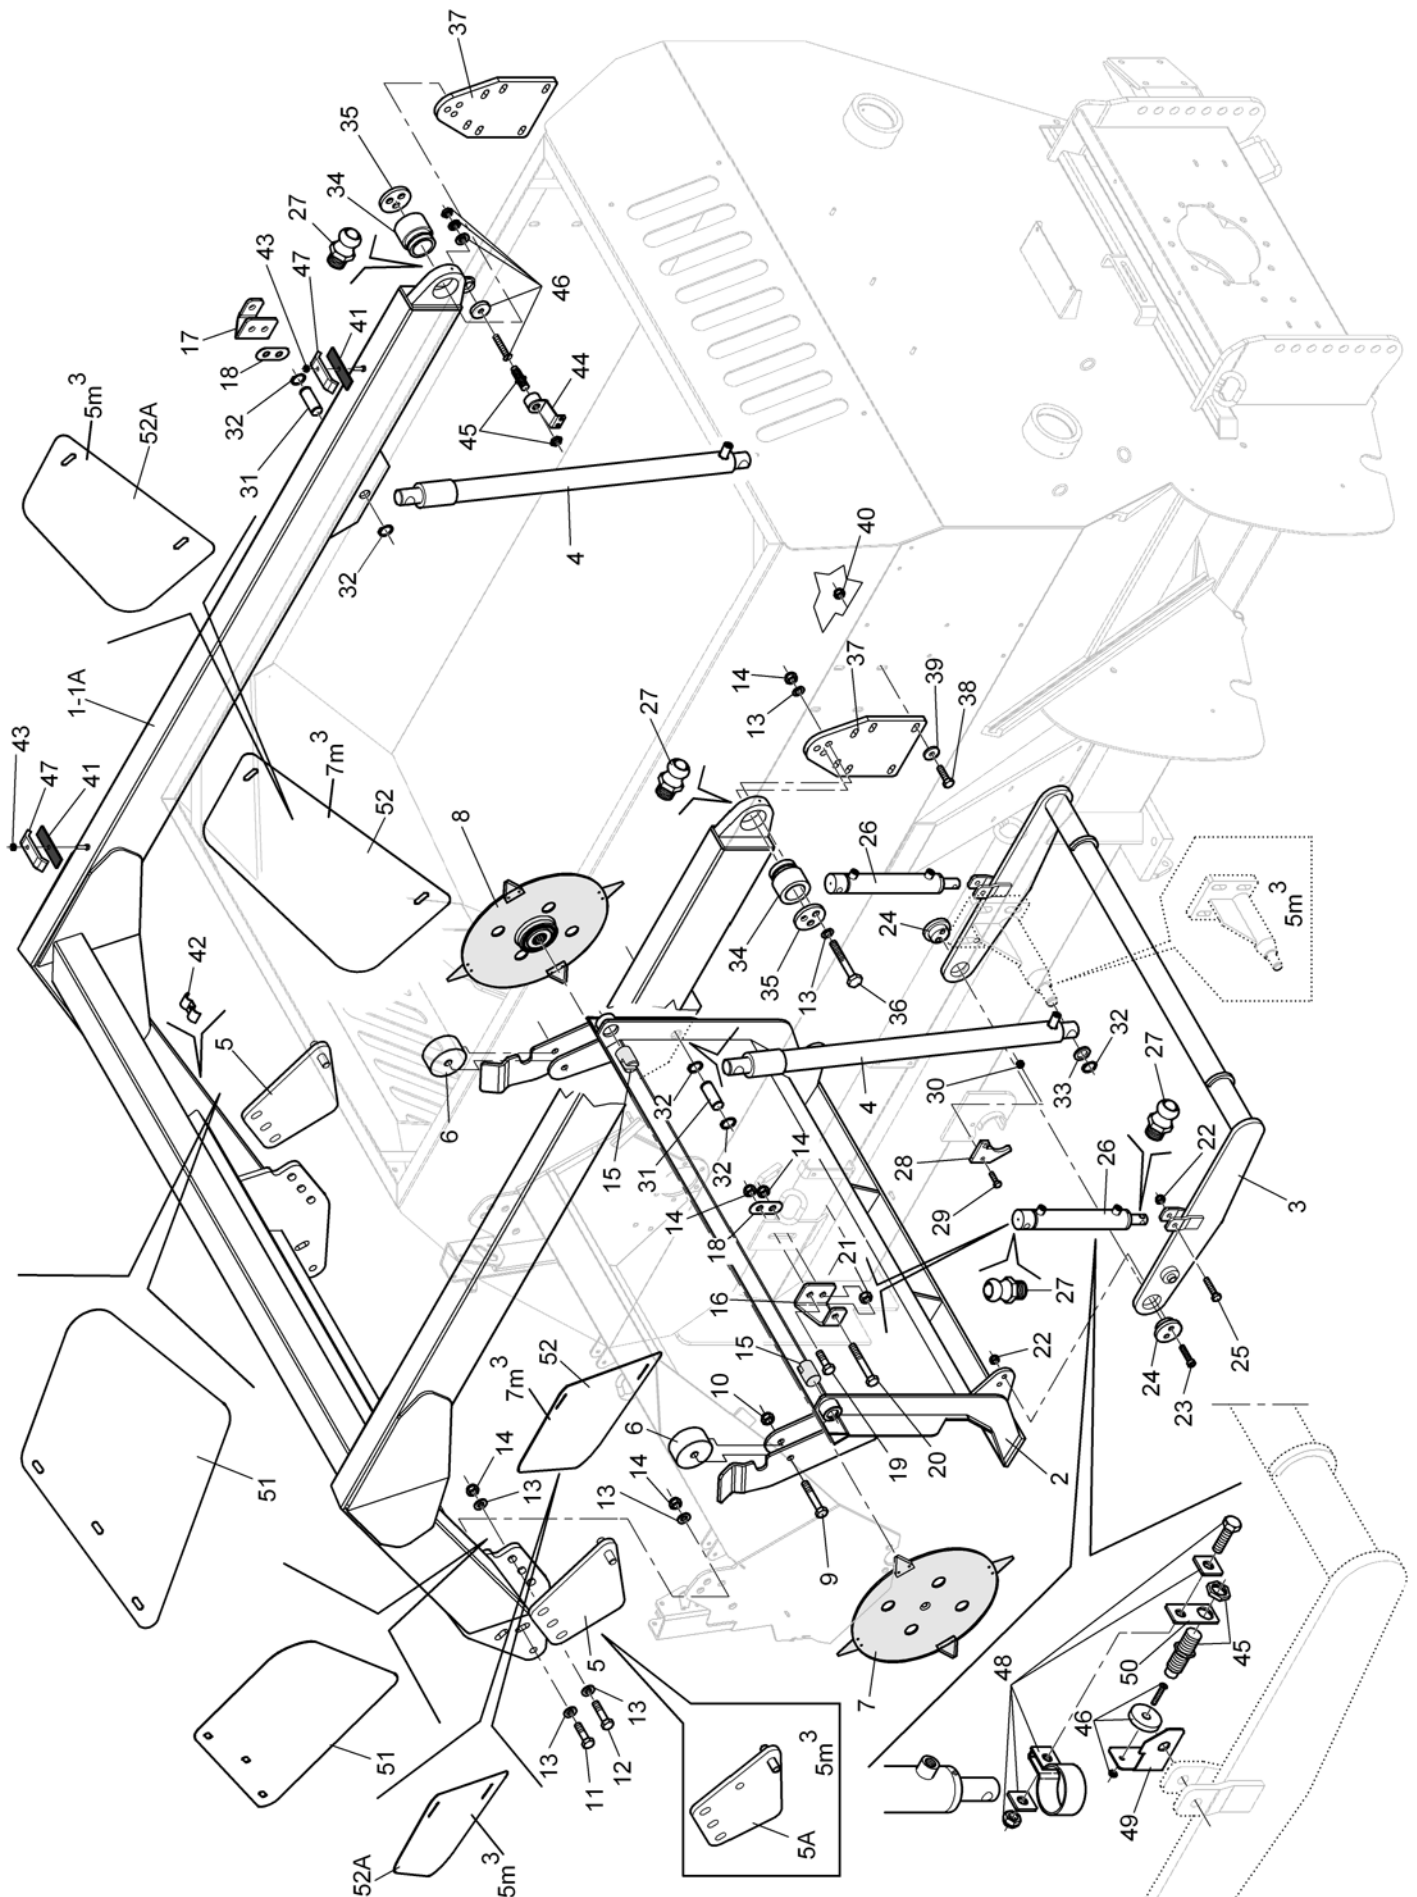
A ABB. Ed.04.08	TELAIO FRESA DS 9/16m³ FRAME MILLING MACHINE DS 9/16m³ RAHMEN FRÄSE DS 9/16m³ CHÂSSIS FRAISEUSE DS 9/16m³ BASTIDOR FRESADORA DS 9/16m³
